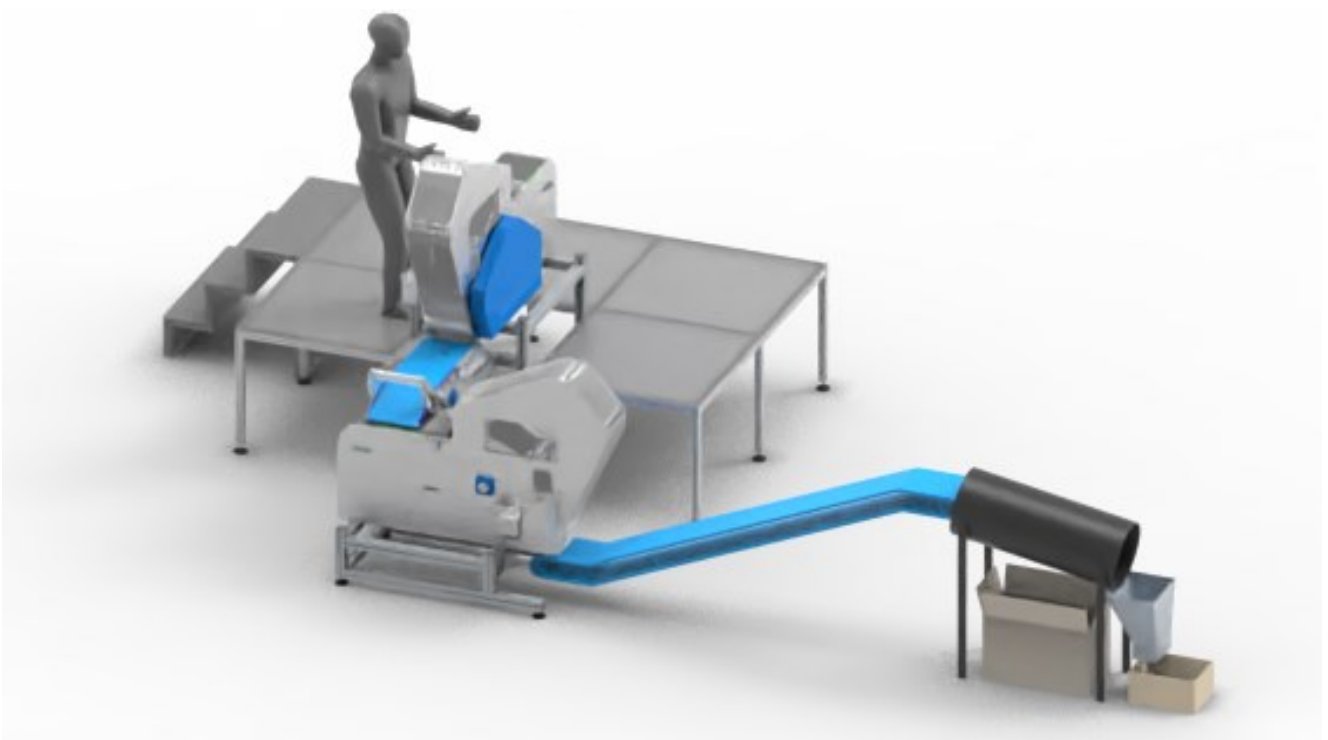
Layout complessivo del blocco 1 (vista assonometrica 2)
